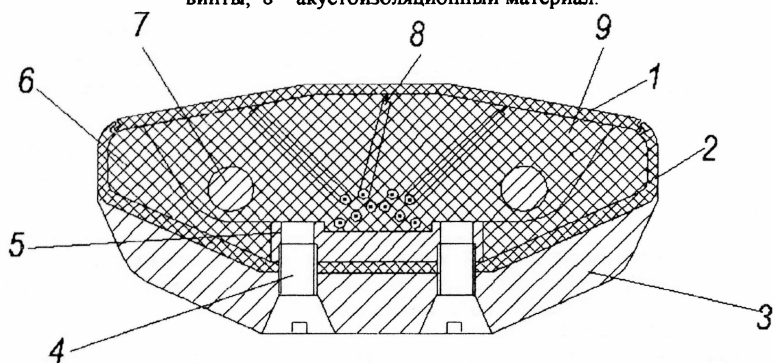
Поперечное сечение излучателя на основе СПКП: 1 – моноблочный СПКП; 2 – корпус излучателя; 3 – полукорпус; 4 – винты; 5 – балка; 6 – вкладыши; 7 – шпильки; 8 – коммутирующие провода; 9 – акустоизоляционный материал.
